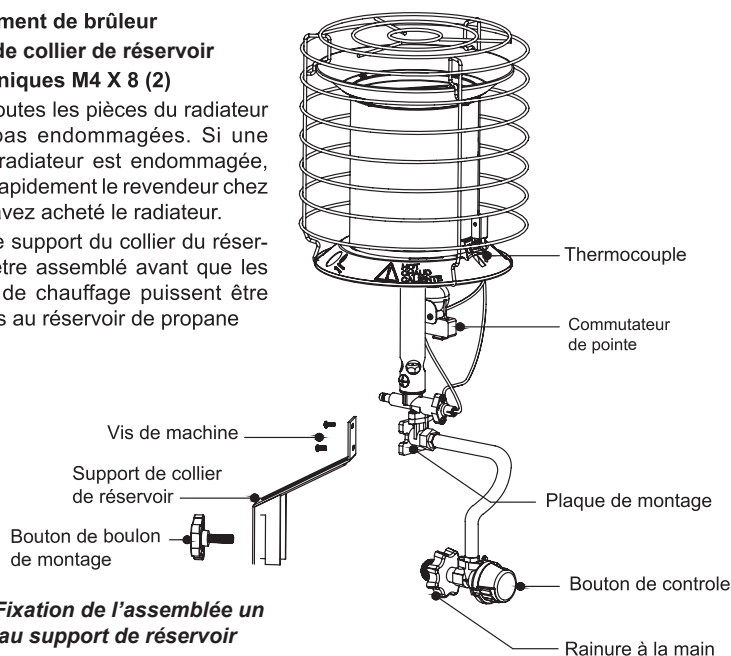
Fixation de l'assemblé un brûleur au support de réservoir
